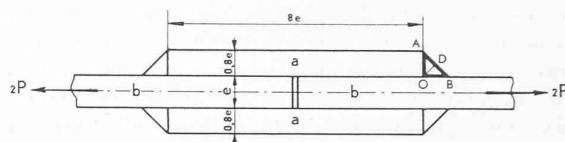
Assemblage soudé par double couvre-joint.
